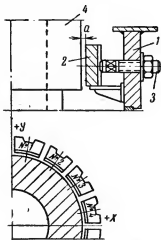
Схема проверки зазоров в подшипнике генератора.
